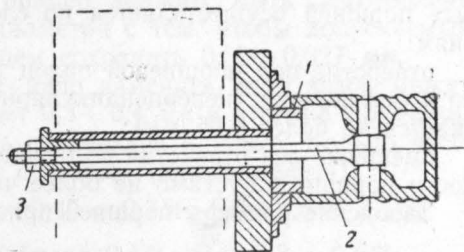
Приспособление для проточки поршневых канавок на токарном станке:
